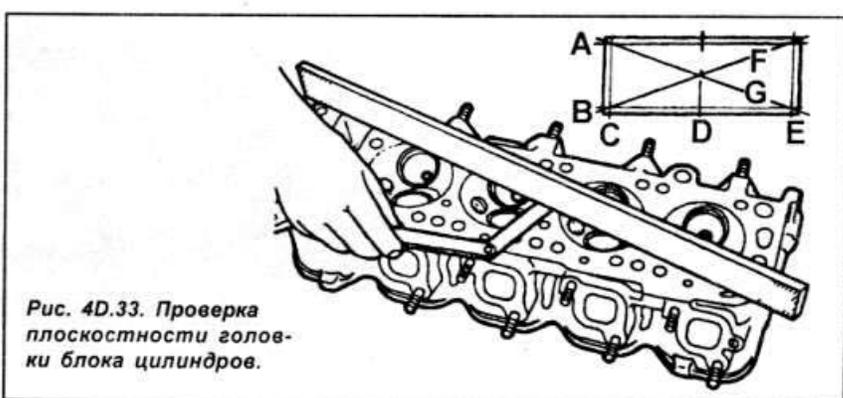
D.33. Проверка плоскостности головки блока цилиндров.
